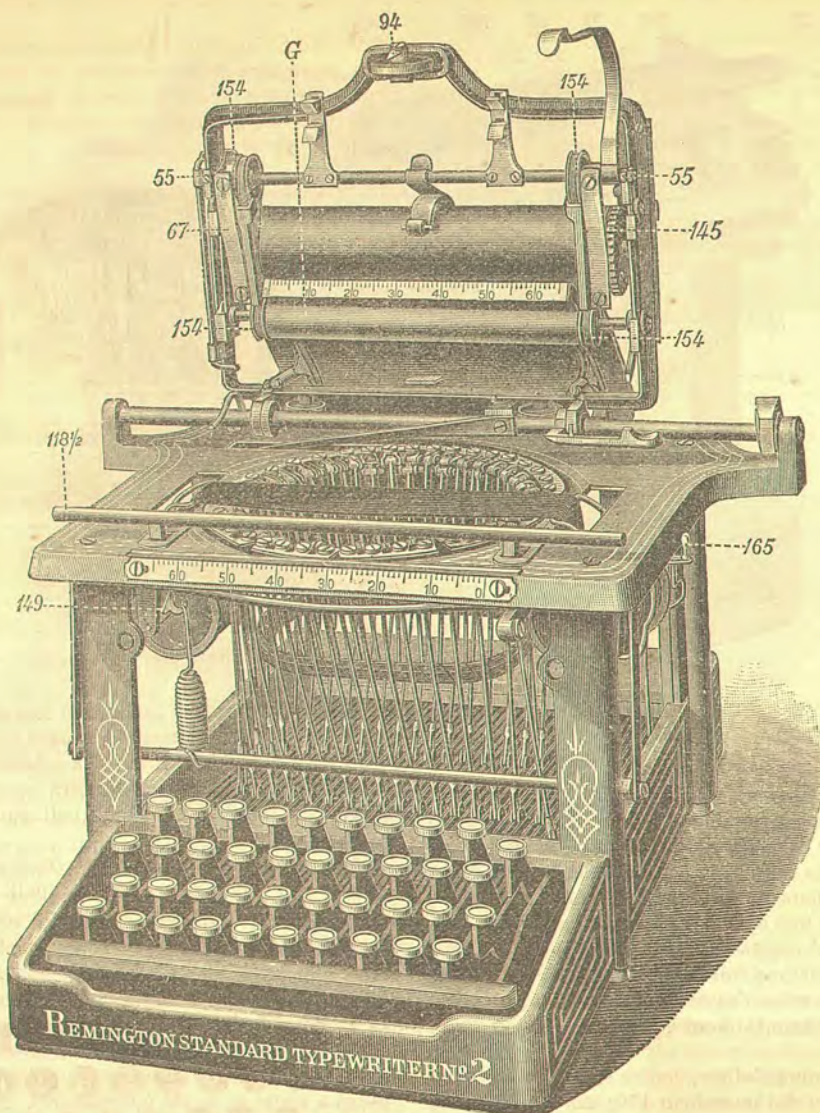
Macchina « Remington », col carrello sollevato.
